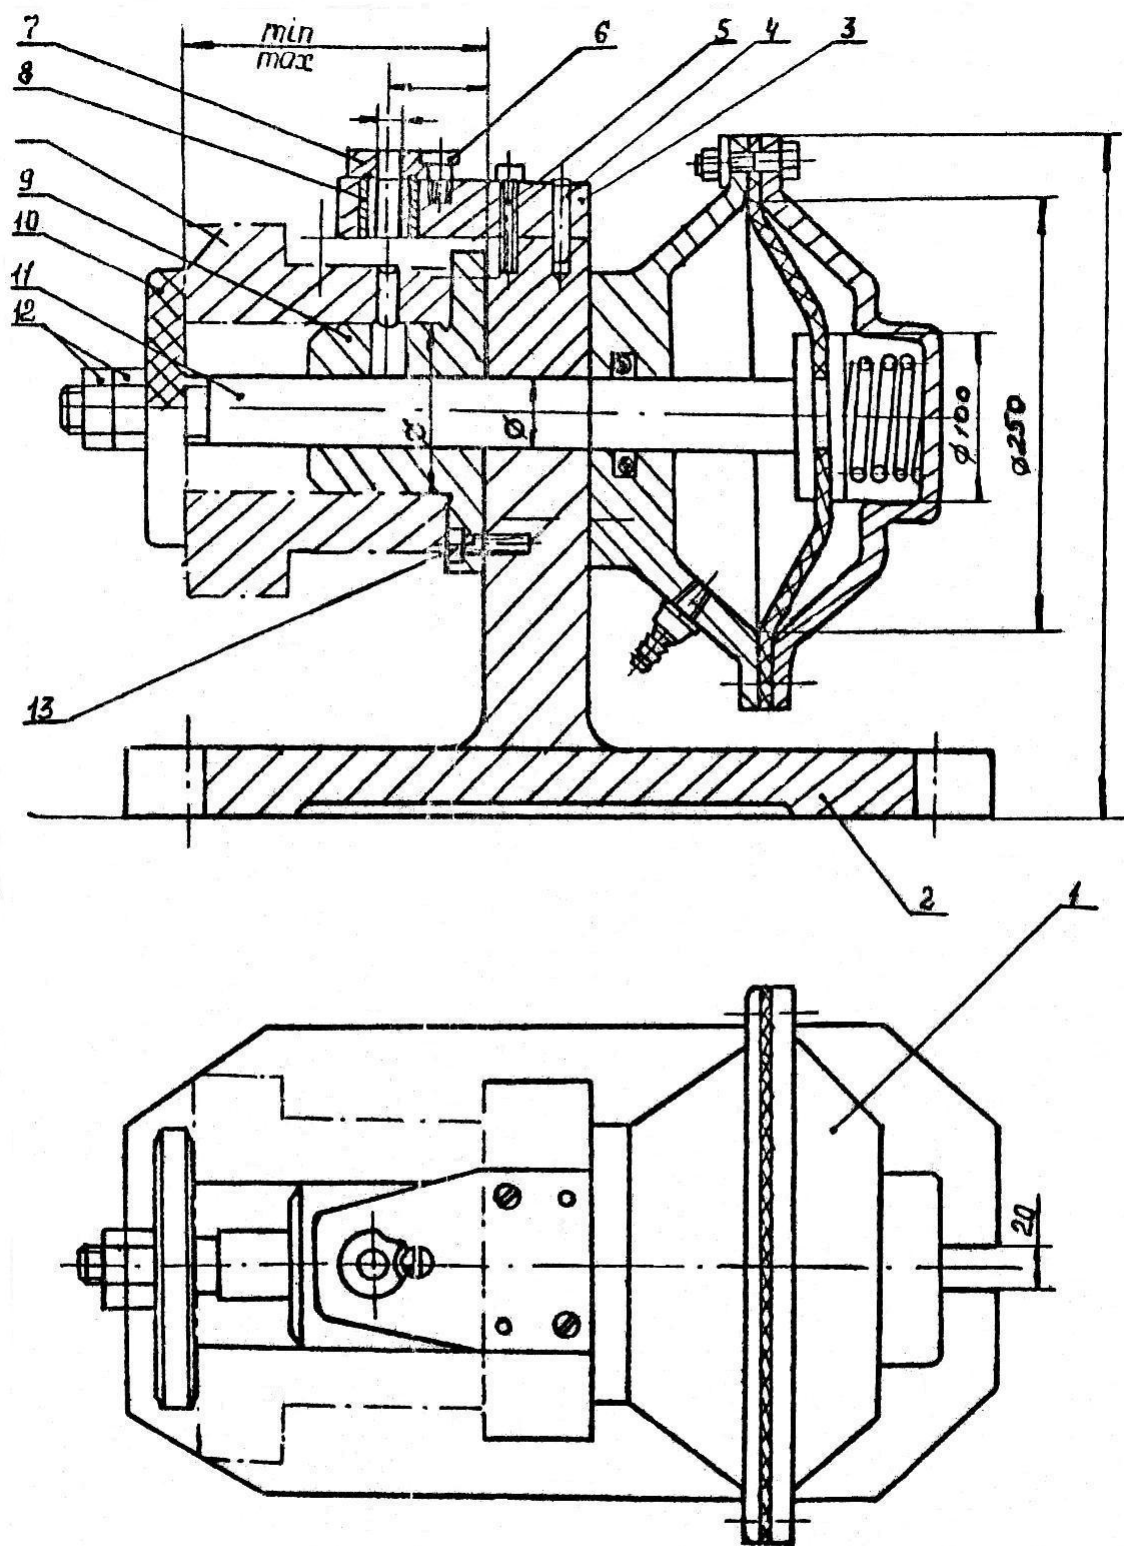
Кондуктор для сверления отвору в деталі "Втулка "
